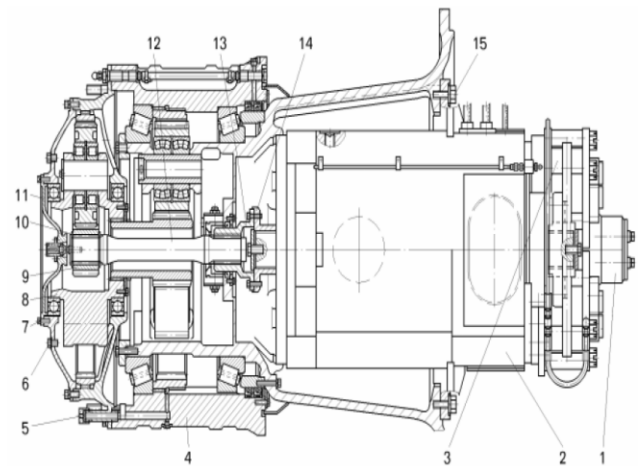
Електромоторколесо: 1 – зупиночний гальмовий механізм; 2 – тяговий електродвигун; 3 – робоча гальмова система; 4 – маточина заднього колеса; 5 – пробка зливного отвору; 6 – пробка заливного отвору; 7, 15 – болти; 8 – редуктор електромотор колеса; 9 – сонячна шестірня першого ряду; 10 – стопорне кільце; 11 – кришка; 12 – торсіонний вал; 13 – фланець торсіонного вала; 14 – фланець тягового електродвигуна
